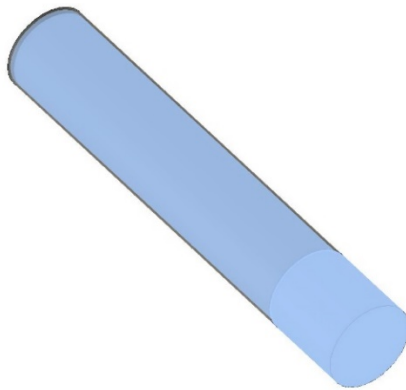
Голубим кольором деталь, сірим заготовка
